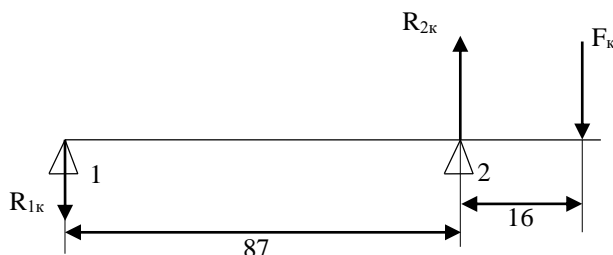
Реакции опор для подшипников быстроходного вала от консольных сил
